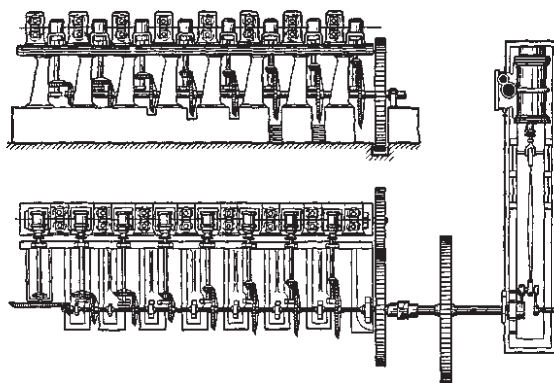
Непрерывный прокатный стан с горизонтальными валками, запатентованный в 1798 г. У. Хезлидайном
